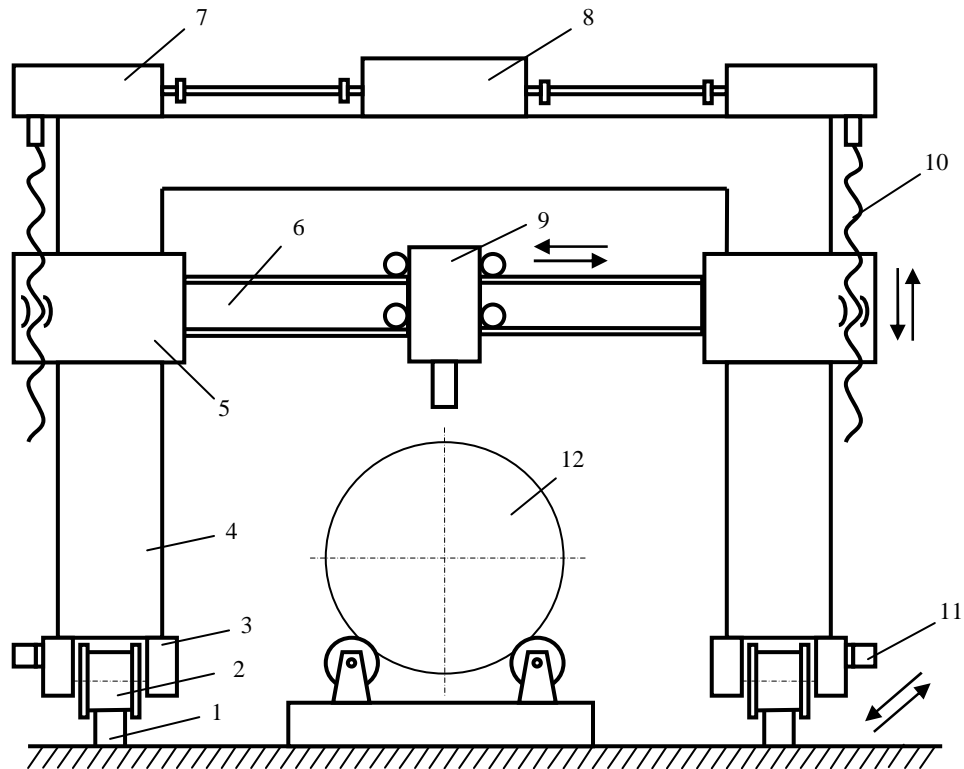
Портальний візок: 1 – рейка; 2 – каток; 3 – платформа; 4 – портал; 5 – каретка; 6 – балка з напрямними; 7 – привод каретки; 8 – електропривод; 9 – зварювальний самохідний автомат; 10 – гвинт ходовий; 11 – привод візка; 12 – виріб.
